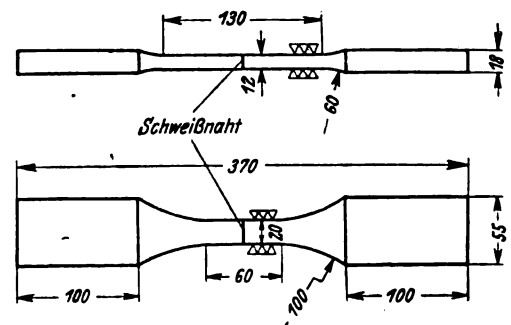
Probstababmessungen für die Zugschweißversuche. (20 mm dicke Bleche.)
